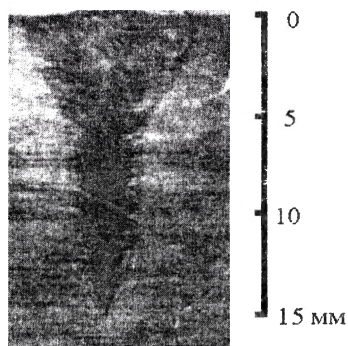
Поперечное сечение сварного шва, полученного ЭЛС
